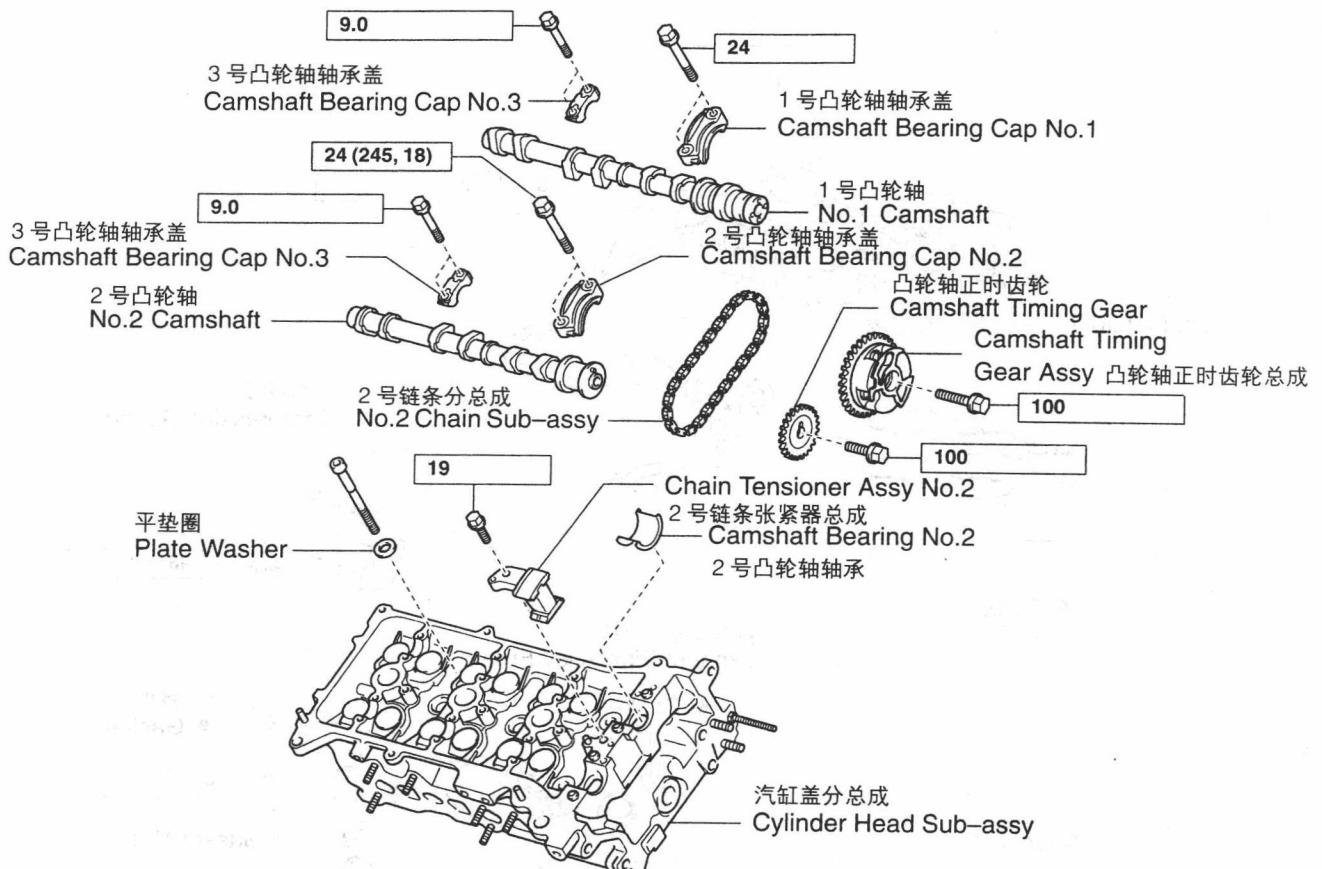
发动机总成 (ENGINE ASSEMBLY) (6)
